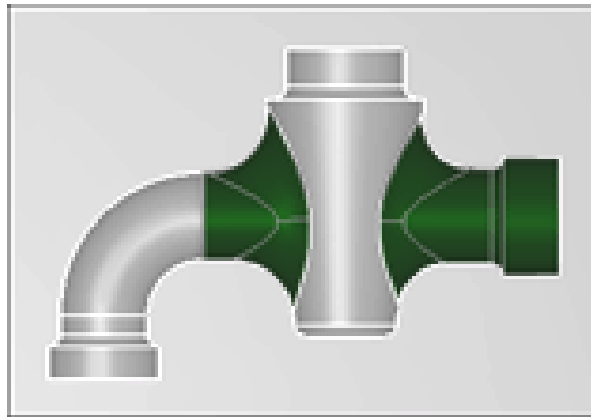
Схема вибору поверхонь фрезерування
